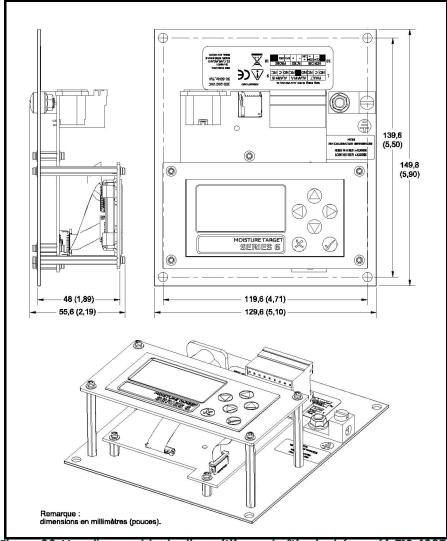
Vue d'ensemble du dispositif sans boîtier (schéma réf. 712-1687)
